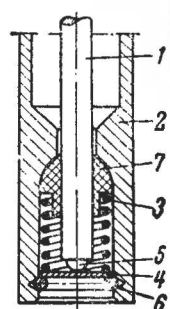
Нижний подшипник узла ведущего вала магнитофона «Юза-5».
